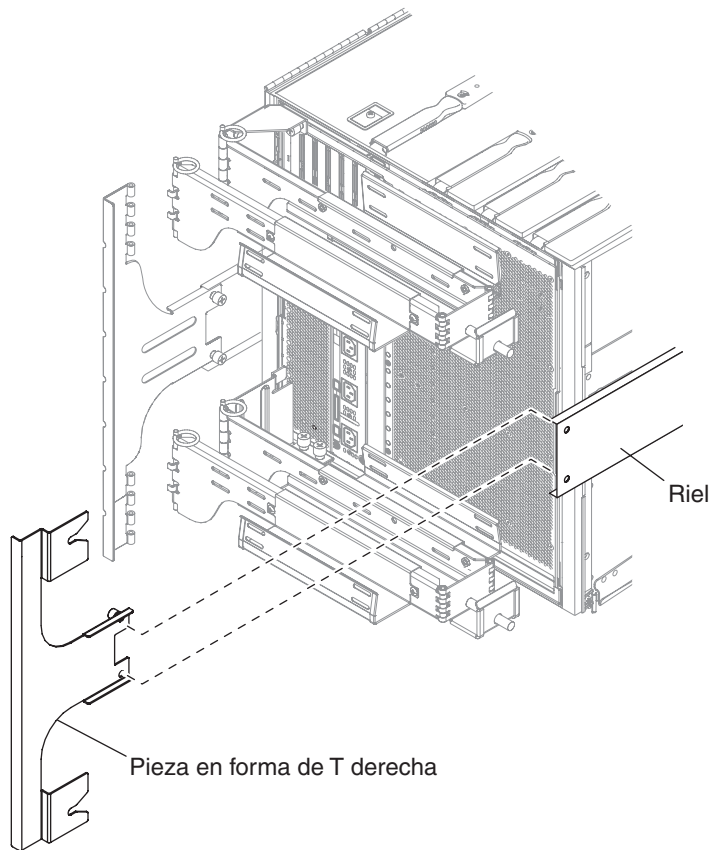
Montaje de la pieza en forma de T derecha
